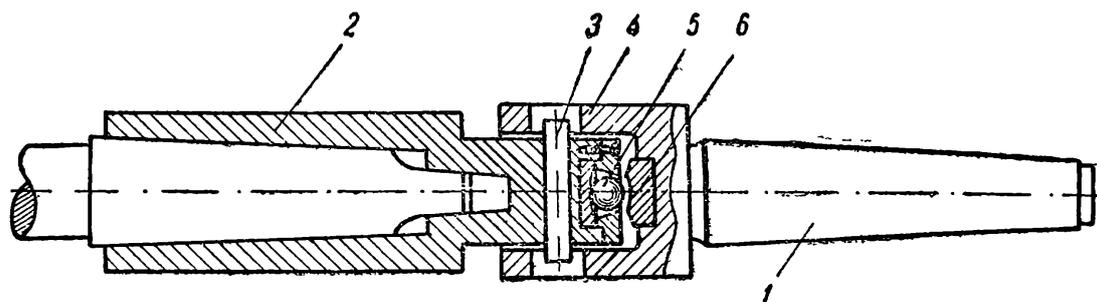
Качающаяся (шарнирная) оправка для крепления развертки на токарном станке:
